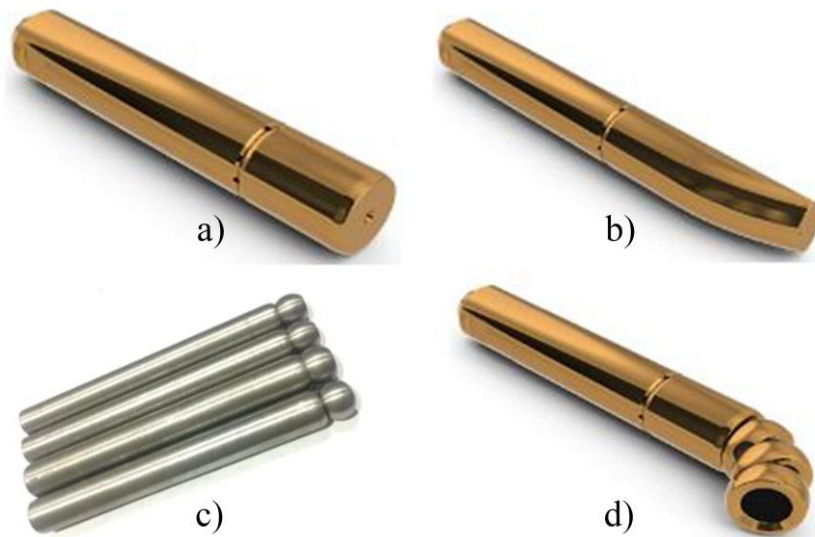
Tipos de mandriles: a) Plug Mandrel v) Form Mandrel c) Single ball d) Multi – ball
